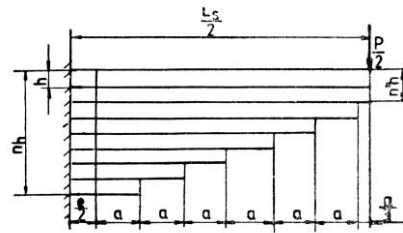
Schema pentru calculul arcurilor trapezoidale simple
